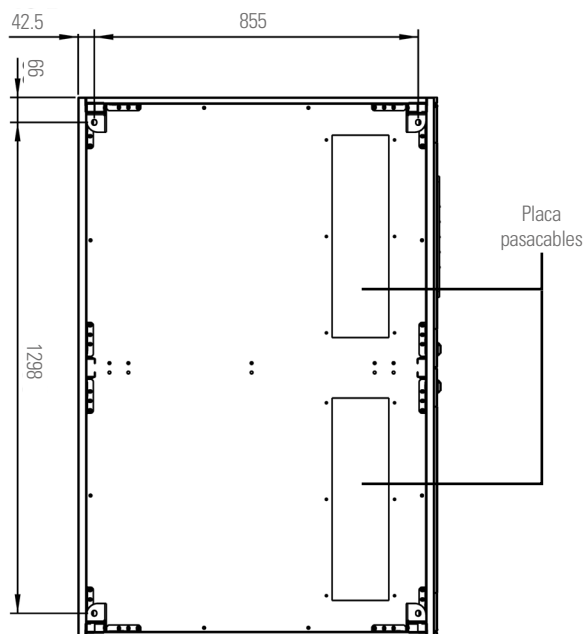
Vista en planta de la base de equipos de 400 kVA.
